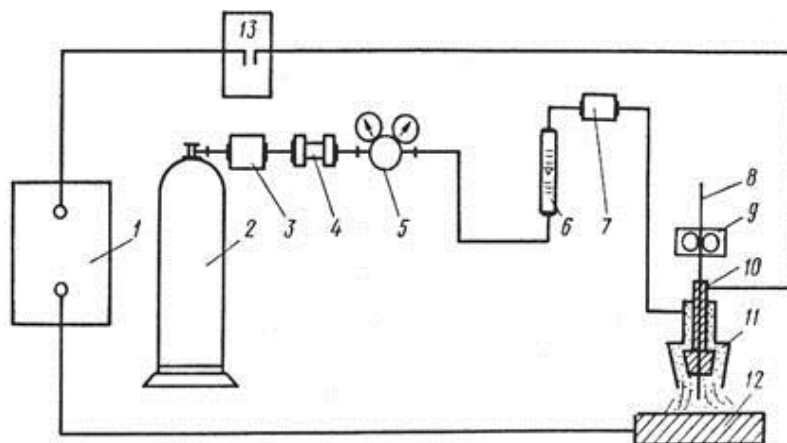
Схема подачи углекислого газа: 1 – Источник сварочного тока; 2 – баллон с углекислотой; 3 – подогреватель газа; 4 – влагоотделитель (осушитель газа); 5 – редуктор газовый; 6 – ротаметр-расходомер; 7 – отсекающий газ и подачи проволоки; 8 – наплавочная проволока; 9 – механизм подачи проволоки; 10 – мундштук; 11 – сопло; 12 – деталь
